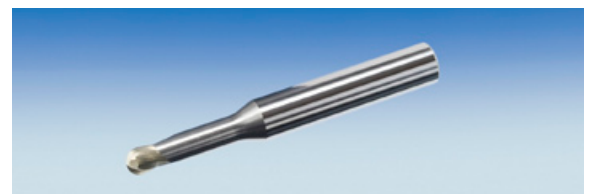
4 mm-Fräser für die Schruppbearbeitung von Chrom-Cobalt.
